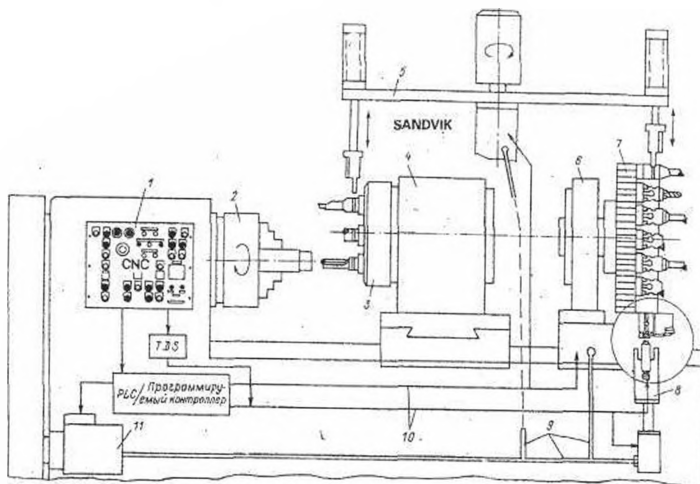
Схема токарного верстата з дисковим інструментальним магазином: 1 – пульт ЧПУ; 2 – патрон; 3 – револьверна головка; 4 – стійка револьверної головки; 5 – автооператор заміни інструмента; 6 – стійка магазину; 7 – дисковий магазин; 8 – адаптер читування я-запису інформації; 9 – гідрорушій; 10 – лінії управління і передачі інформації; 11 – силова гідростанція
